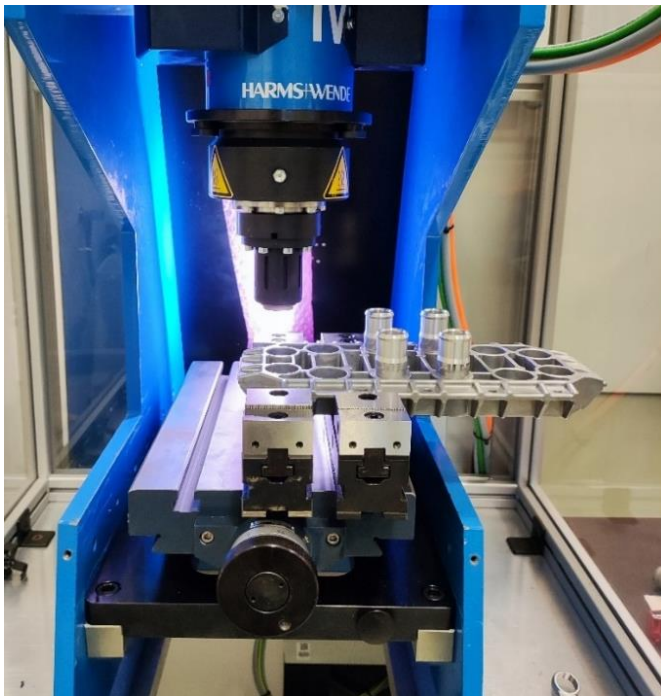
Reibschweißanlage mit Aufspannvorrichtung für Endplatte
